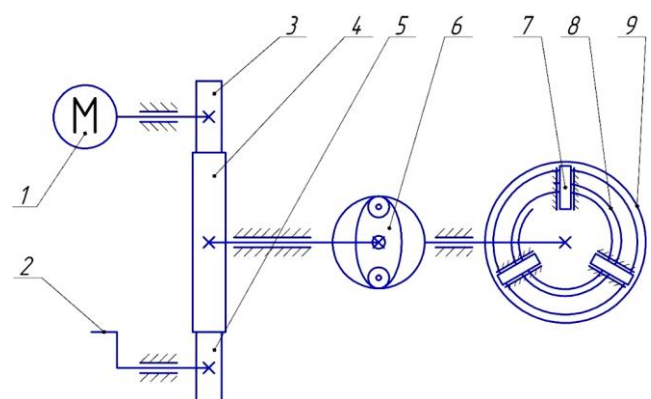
Кинематическая схема электромеханического тормозного устройства: 1 – электропривод; 2 – ручной привод; 3 – выходная шестерня электропривода; 4 – приводная шестерня волнового редуктора; 5 – выходная шестерня ручного привода; 6 – волновой редуктор; 7 – кулачки; 8 – спиральный диск; 9 – контактная стенка
